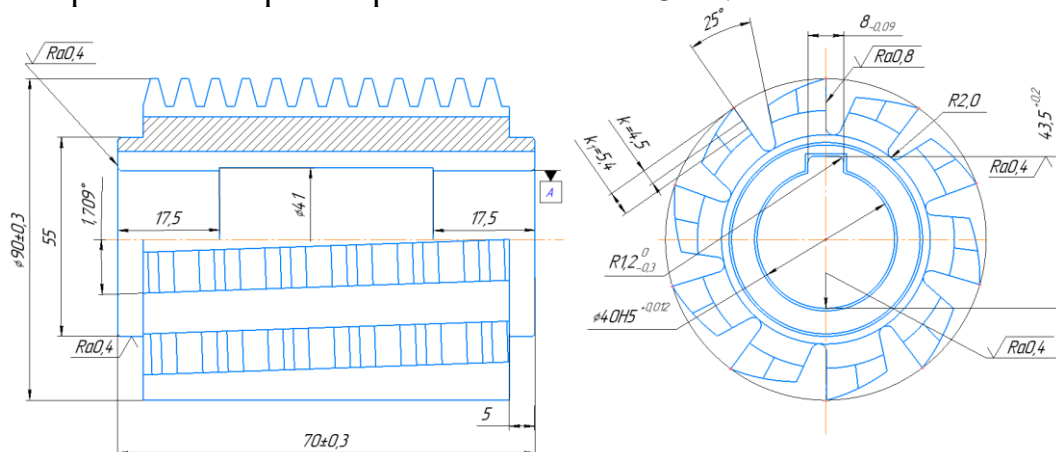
Чертеж чистовой червячной зуборезной фрезы
